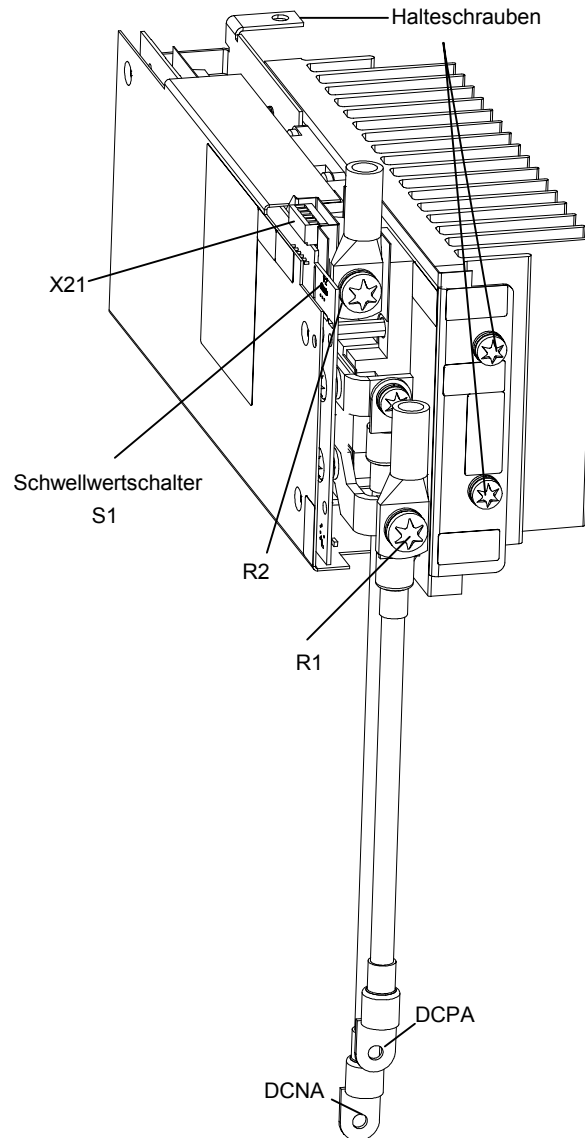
Braking Module für Active Line Module / Motor Module, Baugröße FX
